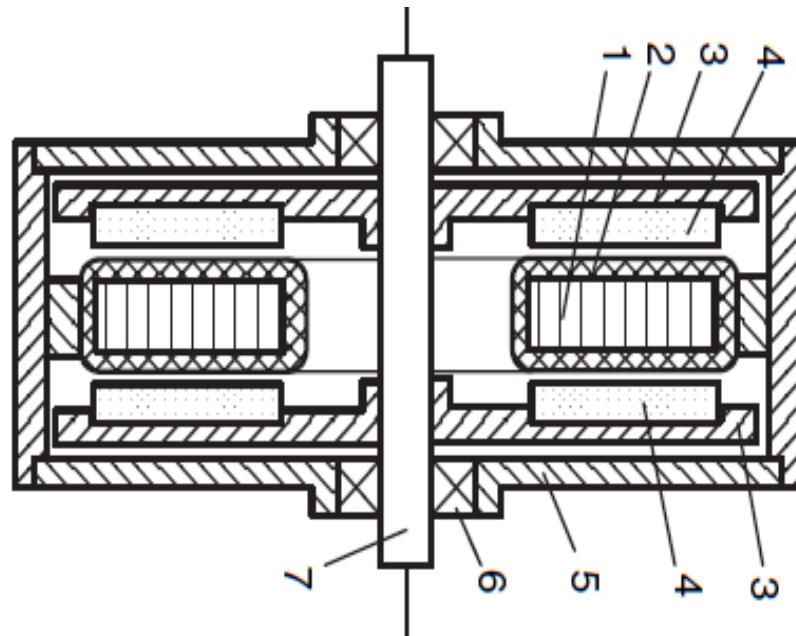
Загальний вигляд торцевого генератора із двосторонньою активною поверхнею: 1 – магнітне осердя статора; 2 – обмотка статора; 3 – ротор; 4 – постійні магніти; 5 – корпус; 6 – підшипники; 7 – вал.
